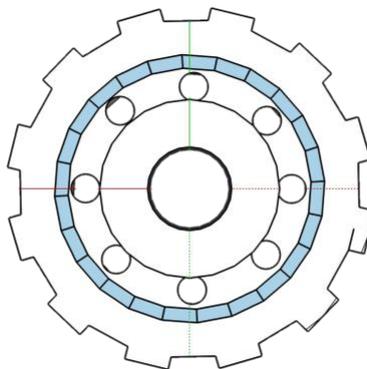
Planta rueda tensora segmentada. Elaboración propia.
